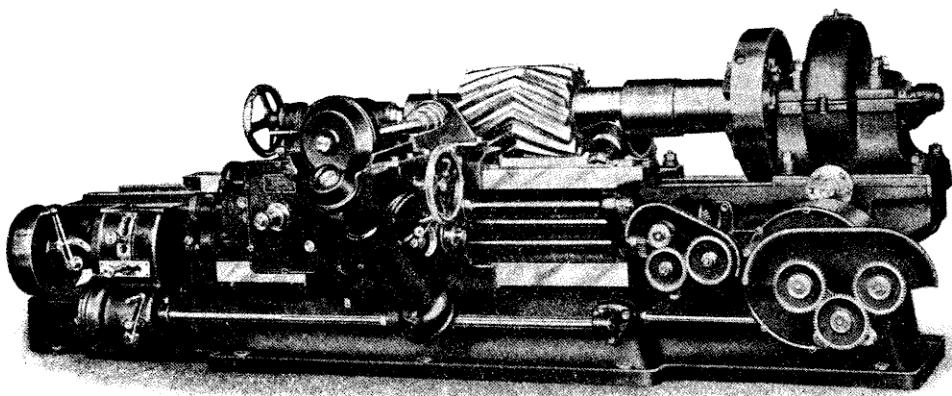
Machine automatique à fraiser les pignons de lamoins.
